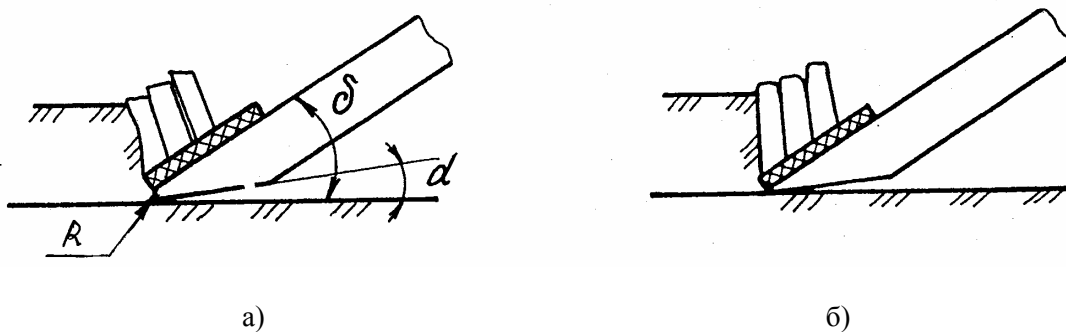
Ріжуча кромка ножа: а) новий ніж; б) самозаточений ніж
